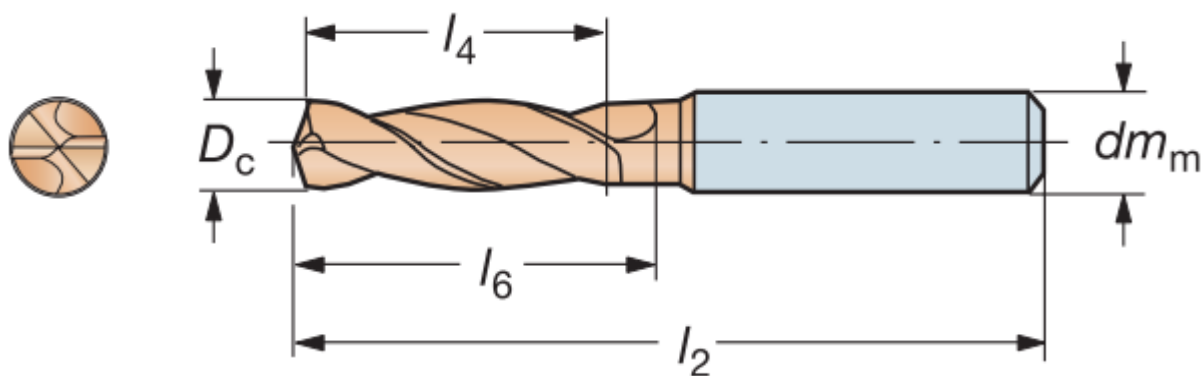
Конструкция сверла R850-0900-10-A1A
